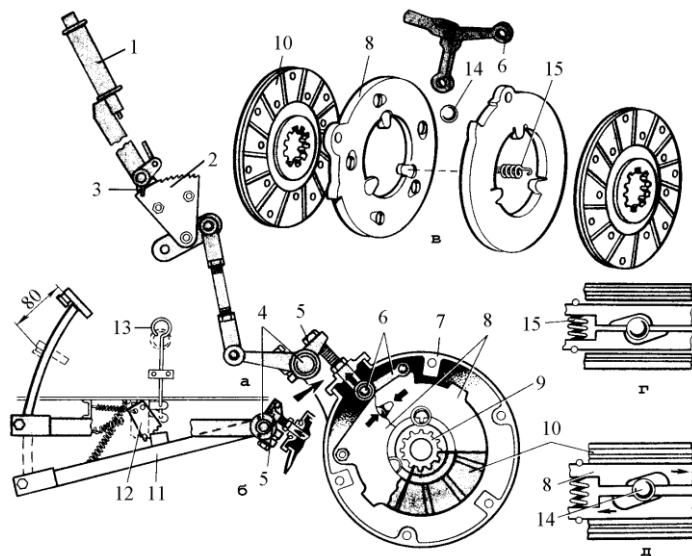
Тормоз дискового типа трактора МТЗ: а – стояночный; б – основной; в – составные части; г – тормоз выключен; д – тормоз включен; 1 – рычаг; 2 – зубчатый сектор; 3 – защелка; 4 – ось промежуточного рычага; 5 – регулировочный болт; 6 – тяги; 7 – кожух; 8 – нажимные диски; 9 – хвостовик ведущей шестерни конечной передачи; 10 – соединительный диск; 11 – педаль; 12 – защелка педали; 13 – тяга включения защелки; 14 – шарик; 15 – пружина
